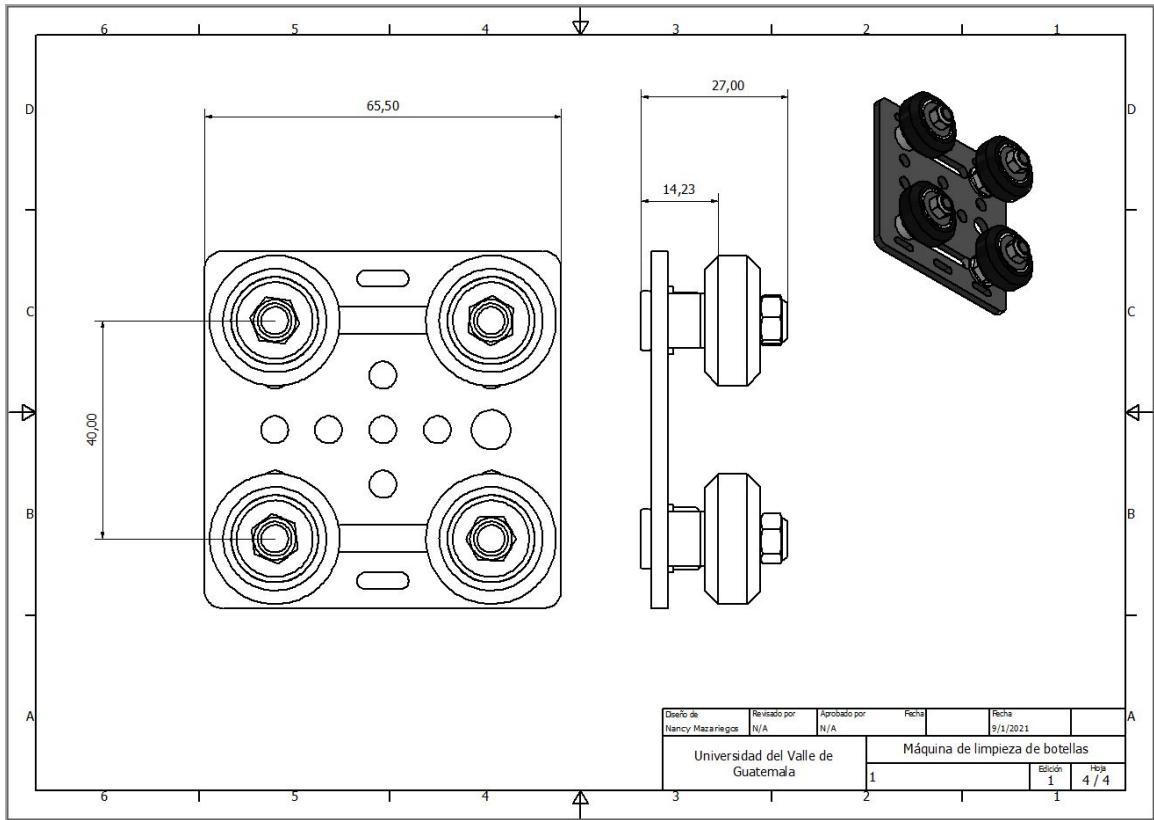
Platina seleccionada para riel vertical, elemento para V-Slot de OpenBuilding
